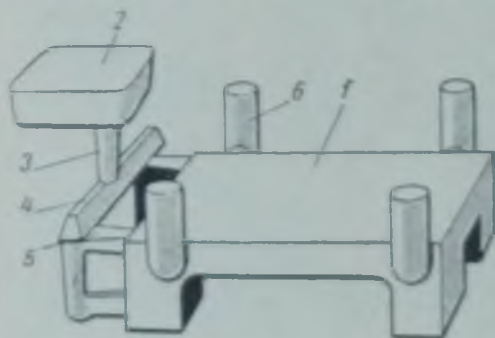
Чугунная отливка с отводными питающими выпорами:
